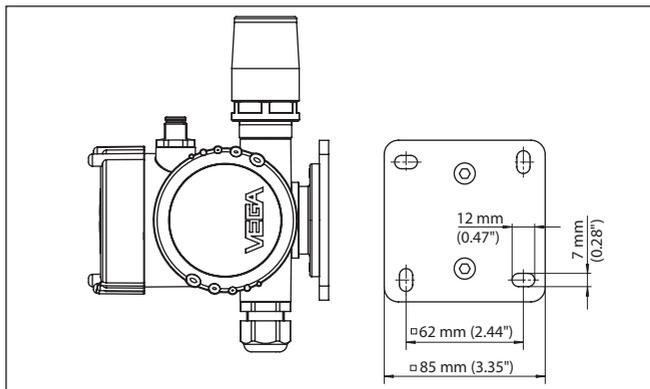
PLICSMOBILE T81 pour montage mural. Plaque de montage vue de dessous.
